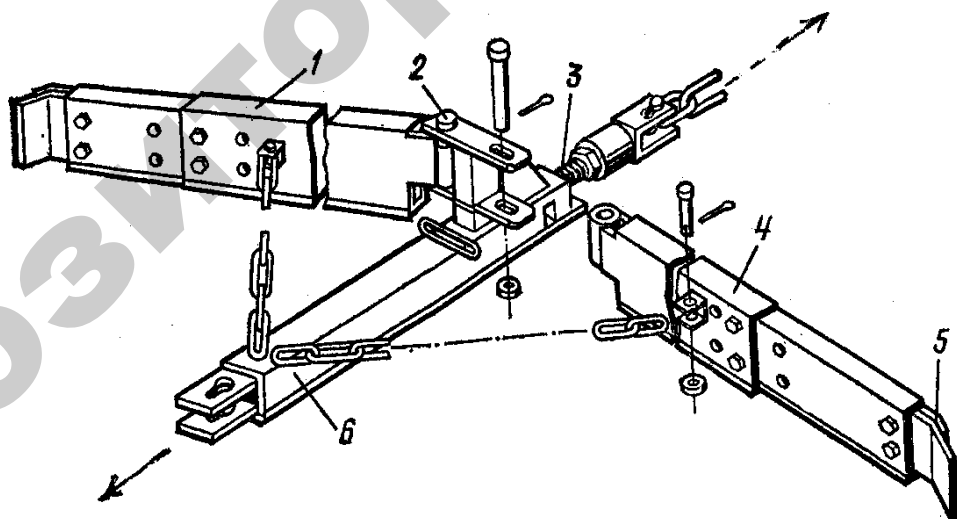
Складывающийся скрепер установки УС-Ф-170:
